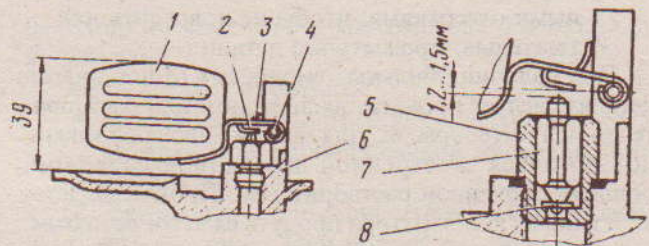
Поплавок с топливным клапаном: 1 - поплавок; 2 - язычок для установки уровня; 3 - ограничитель хода поплавка; 4 - ось поплавка; 5 - седло клапана подачи топлива; 6 - крышка поплавковой камеры; 7 - игла клапана подачи топлива; 8 - уплотнительная резиновая шайба
